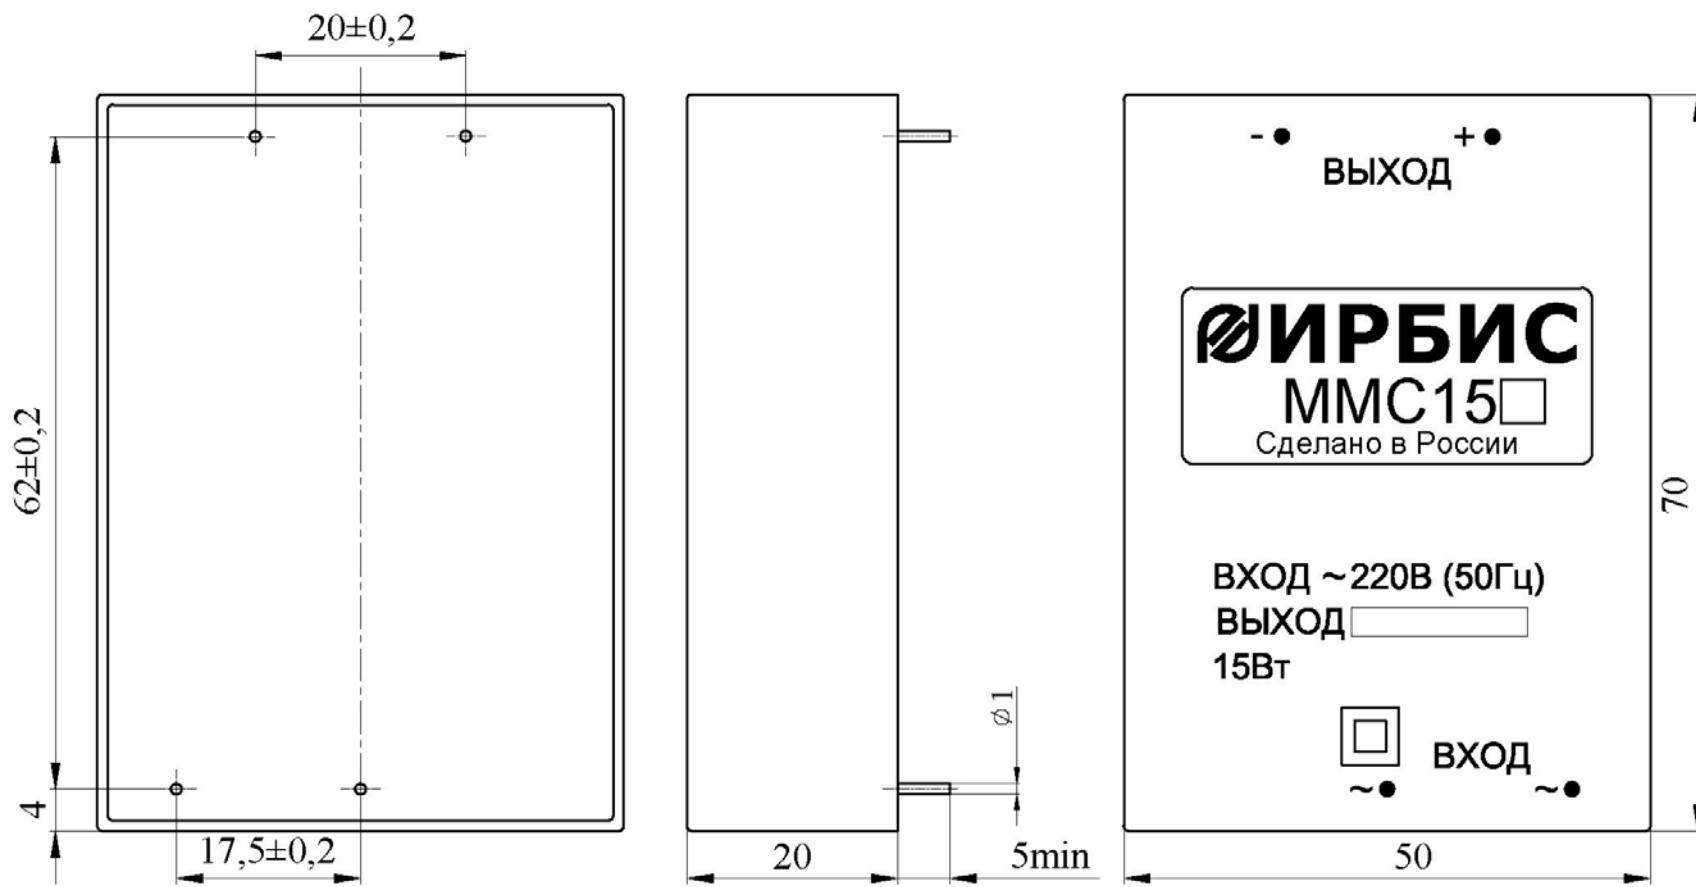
Габаритный чертеж модулей серии MMC15
